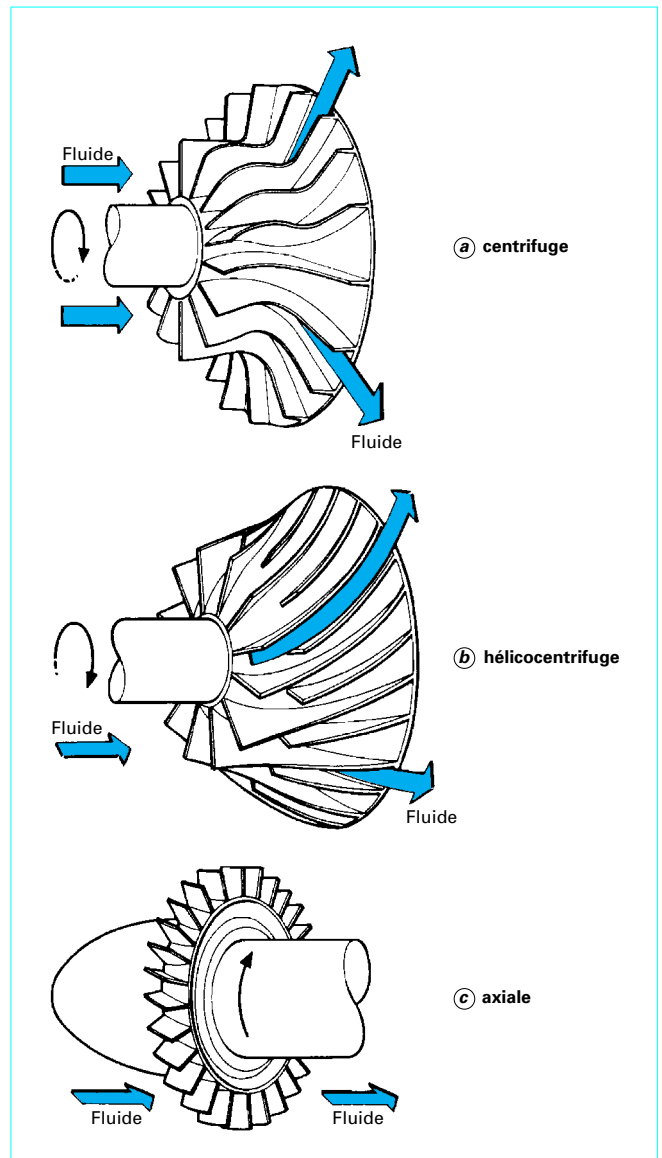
Roue mobile de machines centrifuge, hélicocentrifuge et axiale
